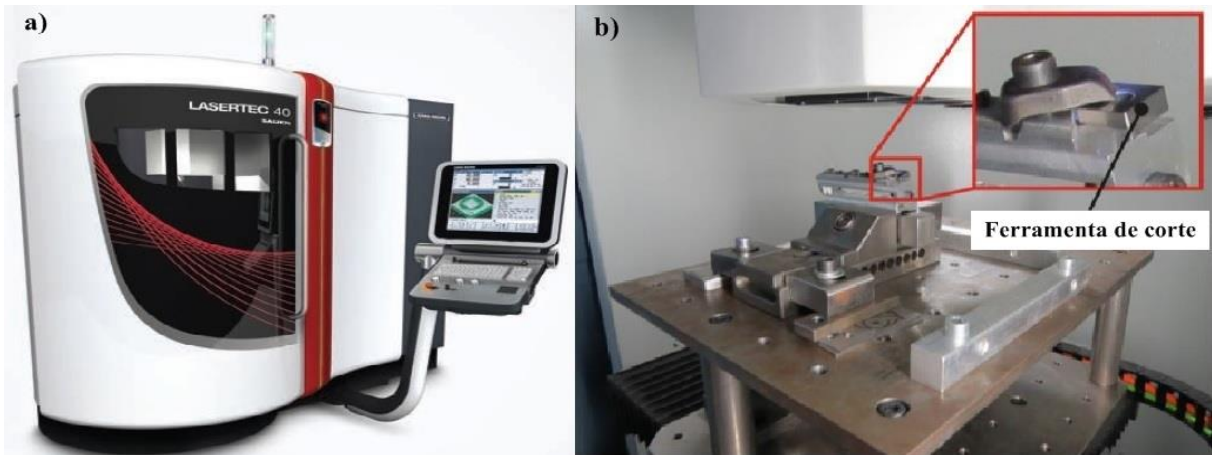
Máquina para usinagem a *laser* (a) parte externa e (b) parte interna.
